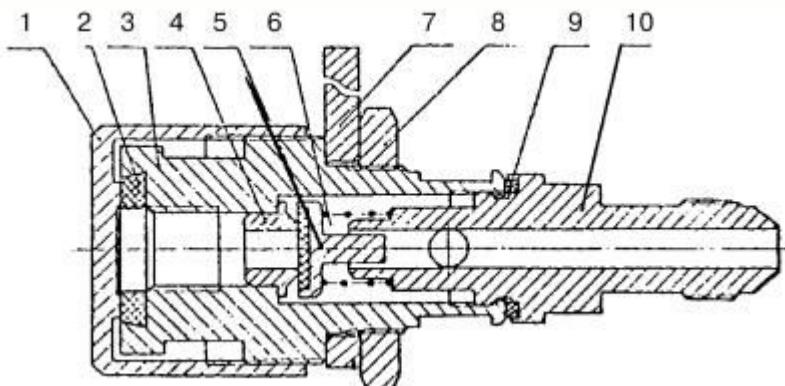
Выносное заправочное устройство: 1 – пробка; 2 – прокладка резиновая; 3 – корпус; 4 – седло клапана; 5 – клапан; 6 – пружина; 7 – кронштейн; 8 – гайка; 9 – кольцо уплотнительное; 10 – штуцер выходной.
